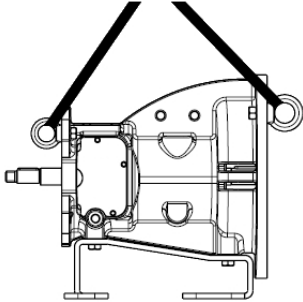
Lagerlaterne A/Illustration 7: Bearing lantern A
